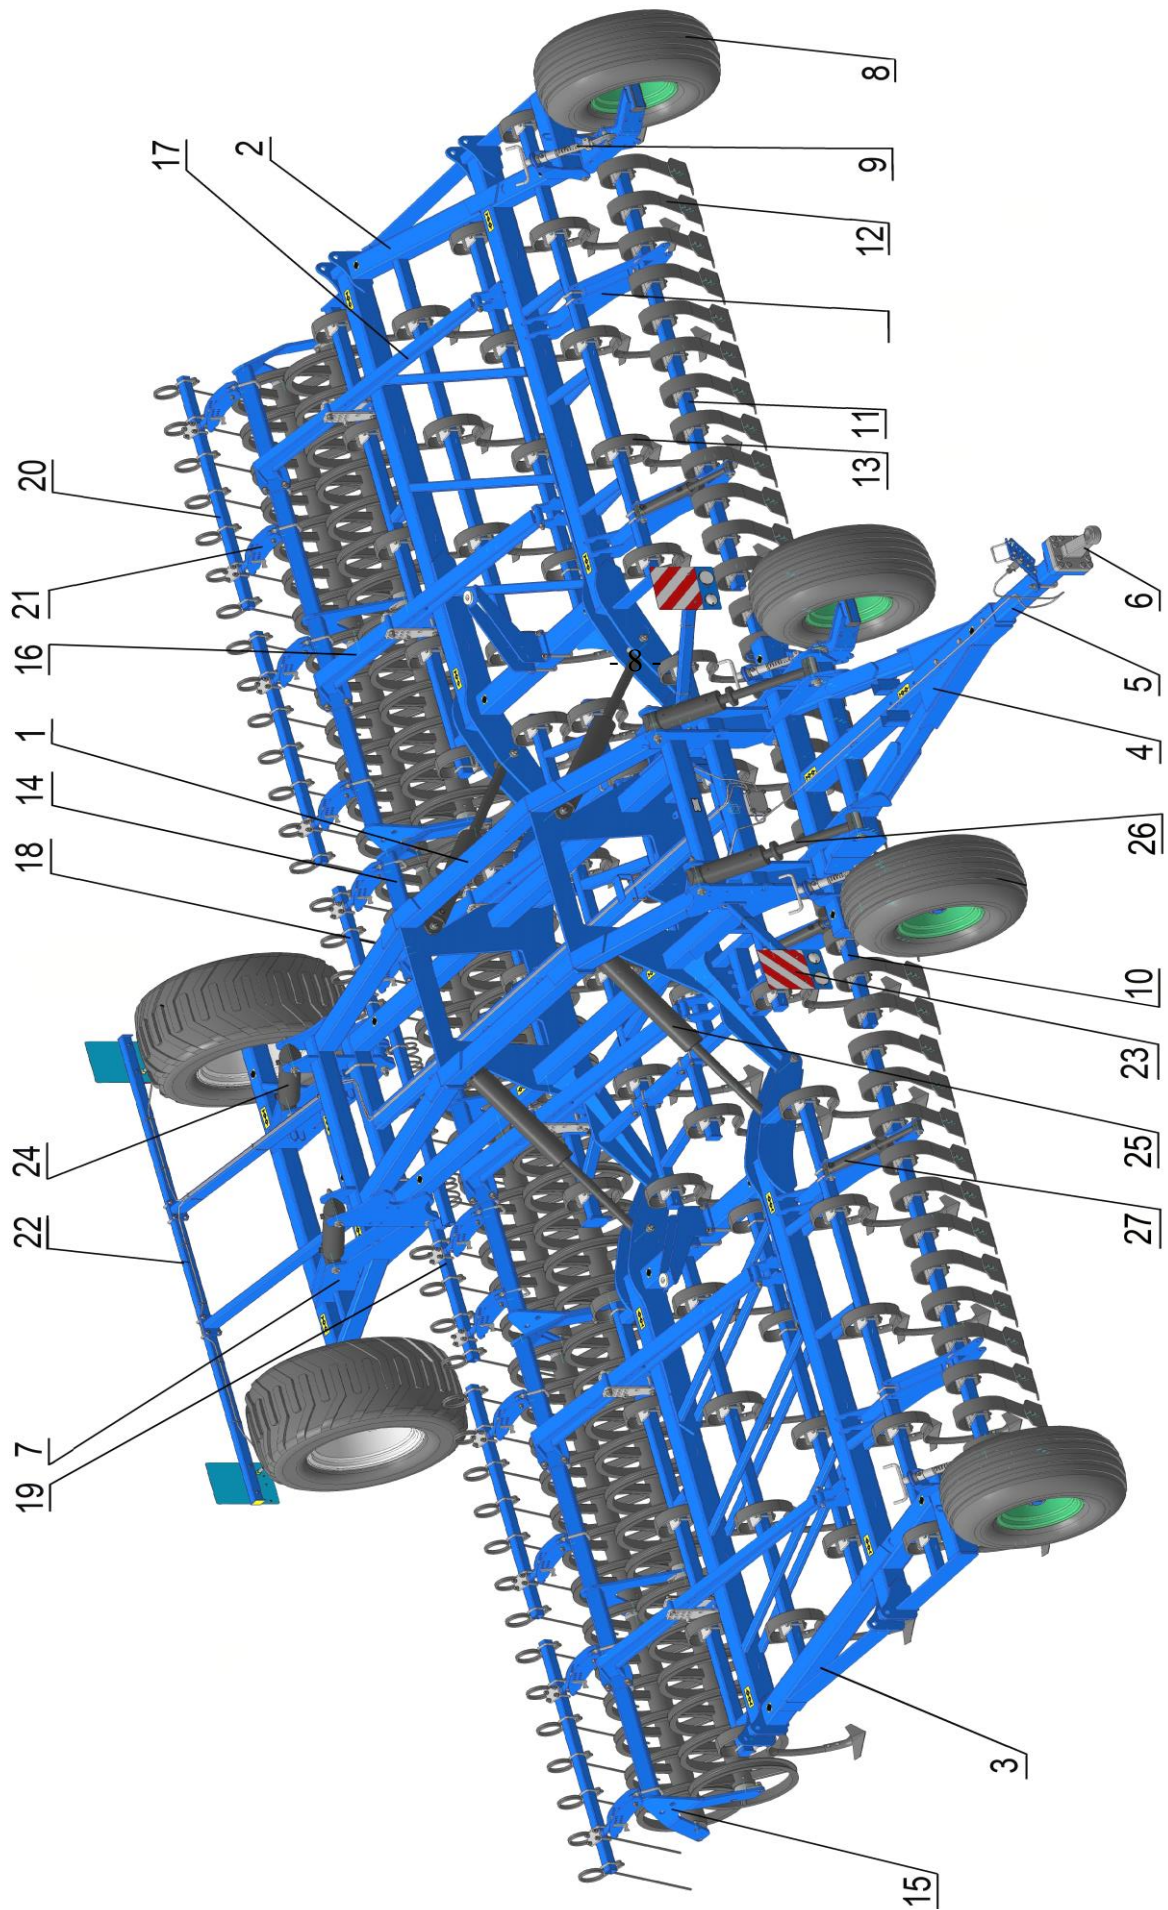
Культиватор прицепной универсальный КПУ-9 (в рабочем положении)
